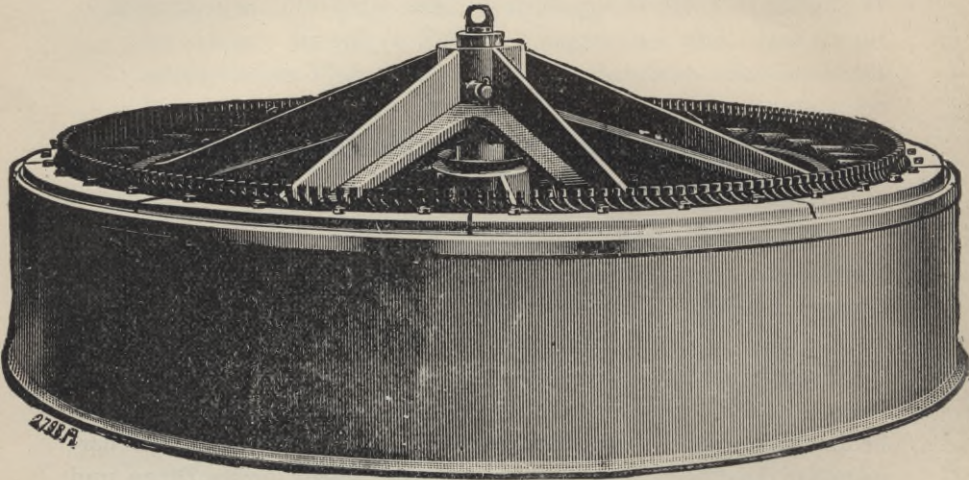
Anker einer Drehstrommaschine mit senkrechter Welle.
